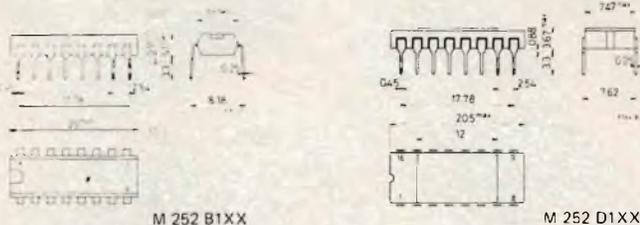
Pianta e profilo dell'IC "M/252", il "batterista elettronico automatico" trattato nel testo.
